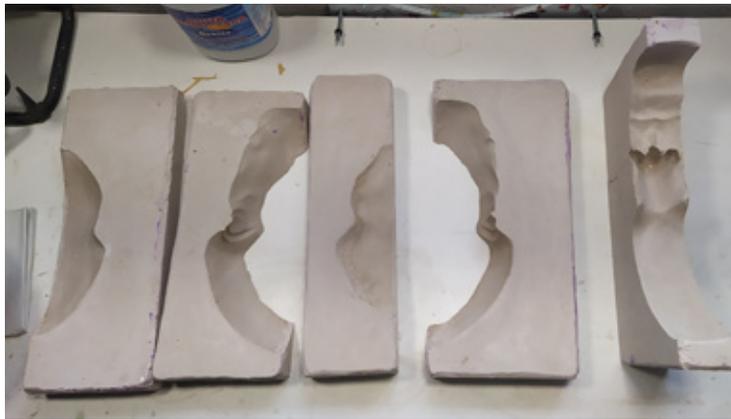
Moldes de escayola de cada pieza del rostro seccionado
